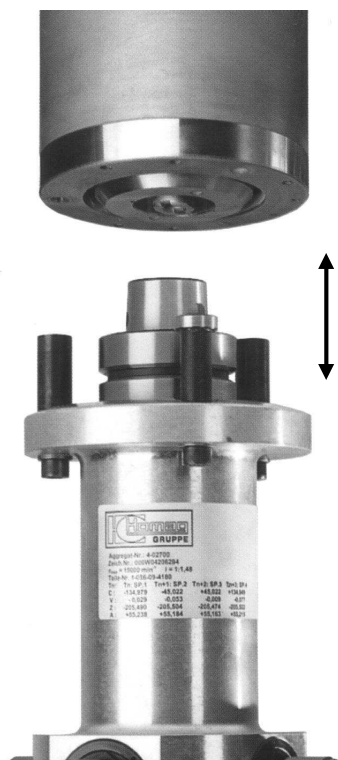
Стыковочный узел оси С и фрезерного агрегата
